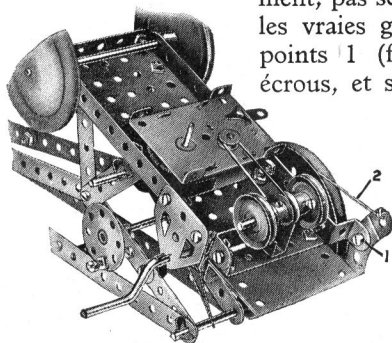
Le châssis de la grue mobile de la fig. 5, vu par en dessous, avec le Moteur "Magic".
